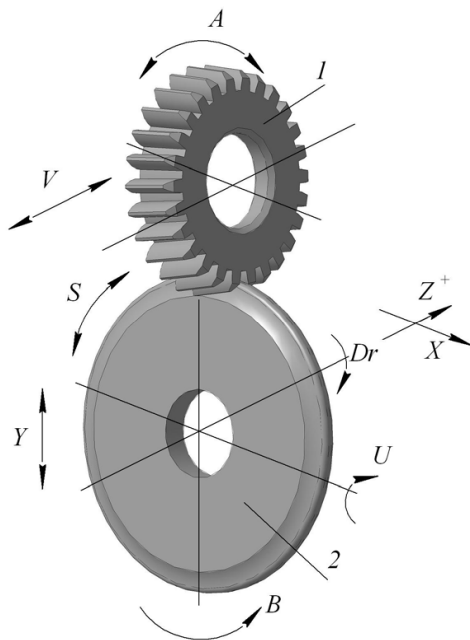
Принципиальная схема обработки на зубошлифовальном станке с ЧПУ: 1 – заготовка; 2 – шлифовальный круг
